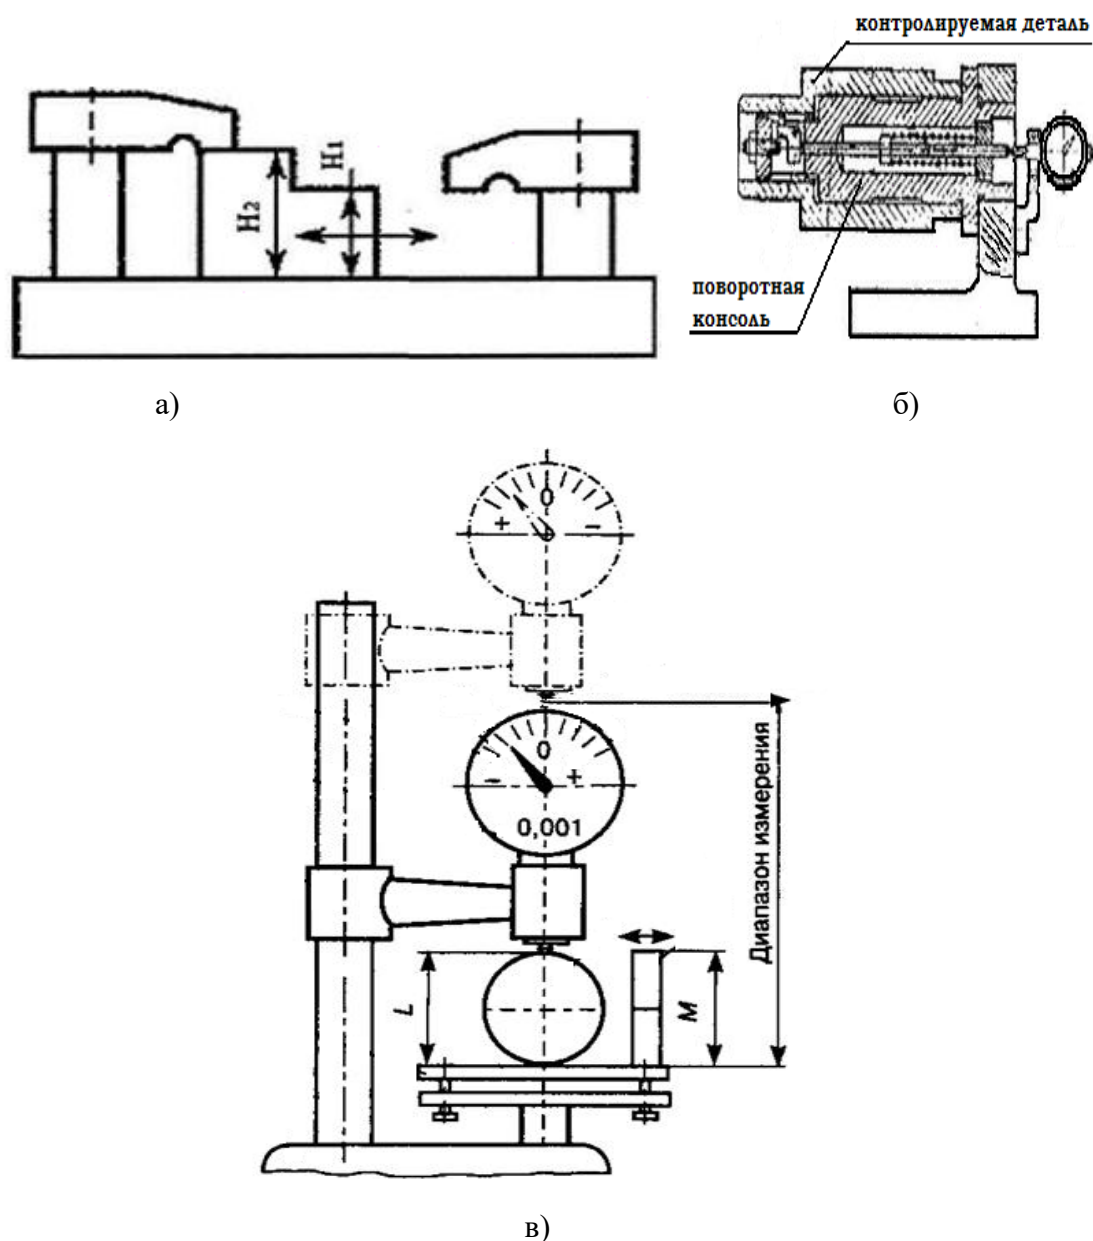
Примеры конструкций контрольных приспособлений:
